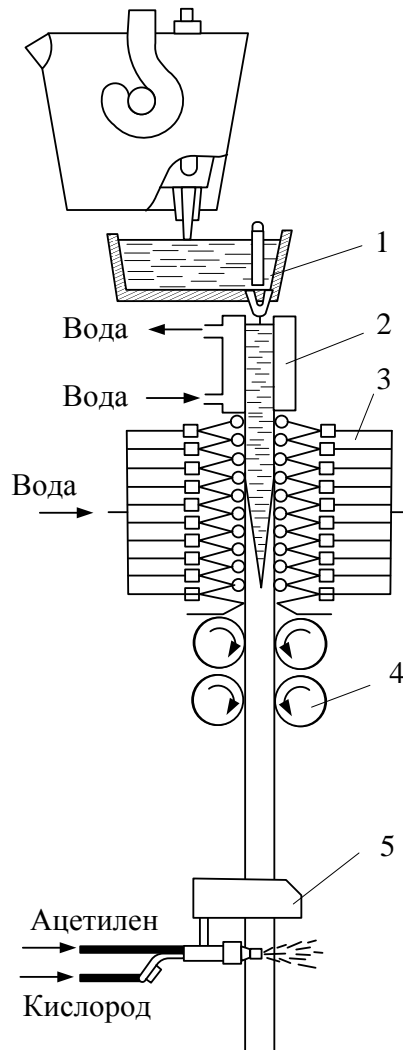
Схема МНЛЗ вертикального типа: 1 – промежуточный ковш; 2 – кристаллизатор; 3 – вторичное охлаждение; 4 – тянущие валки; 5 – газорезка
